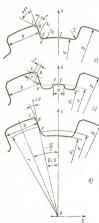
Профили шлицевых валиков с параллельными боковыми сторопами
